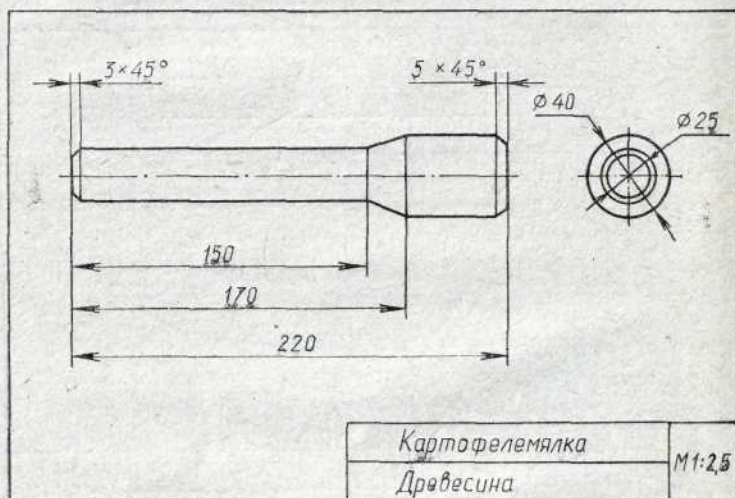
Чертеж цилиндрической детали более сложной формы.
